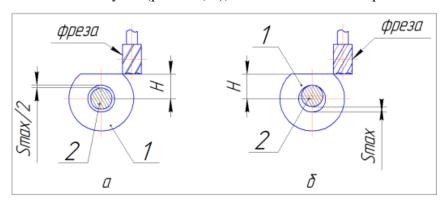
Установка на цилиндрический палец конструкторская база – ось заготовки: а – оси заготовки 1 и оправки 2 совпадают; б – оси заготовки 1 и оправки 2 не совпадают
